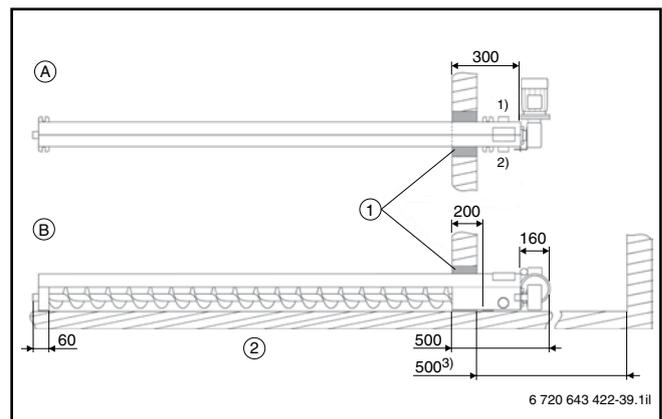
Vista dall'alto e laterale della vite (quote in mm)
